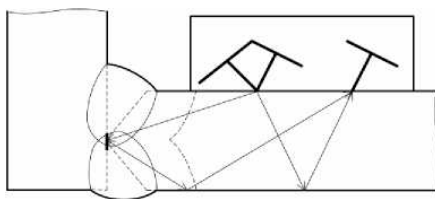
Схема контроля угловых сварных соединений специализированным преобразователем СП5-75КУБ.
